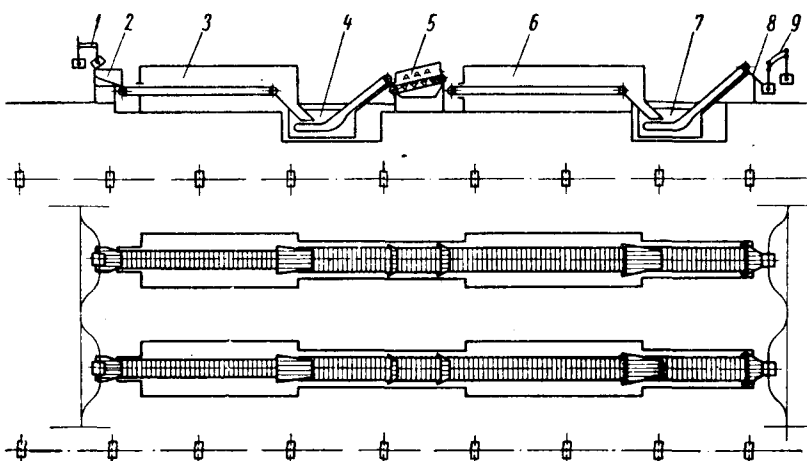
Схема одного из пролетов автоматизированного термического цеха: 1 — толкающий конвейер; 2 — загрузочный бункер; 3 — печь для нагрева под закалку; 4 — закалочный бак; 5 — моечная машина; 6 — печь для отпуска; 7 — бак для охлаждения деталей после отпуска; 8 — разгрузочный лоток; 9 — толкающий конвейер.
